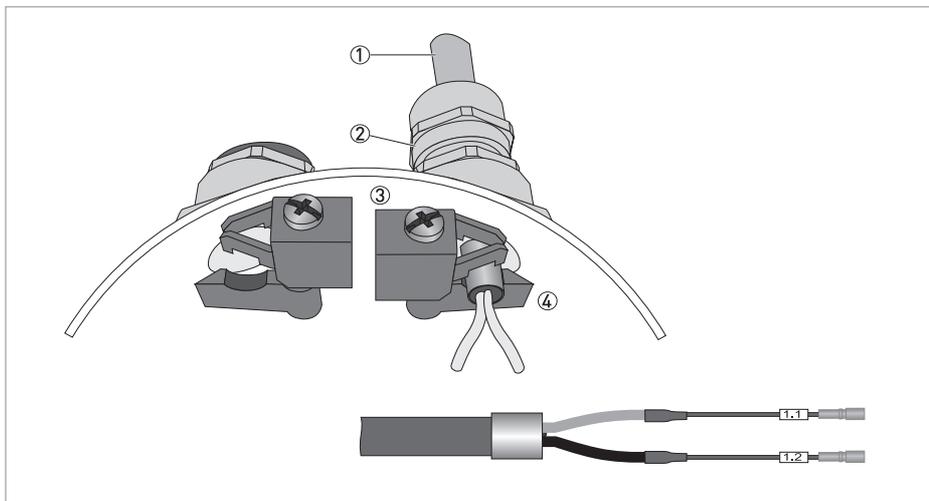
Inserire il cavo e fissarlo con morsetto sulla boccola di schermatura
